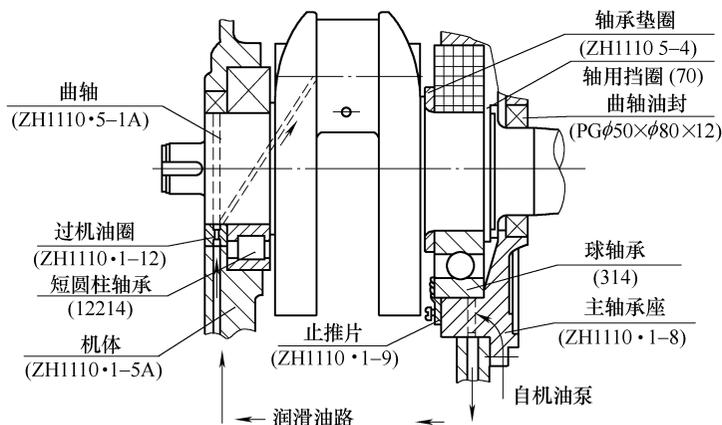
ZH1110 型、ZH1115 型柴油机曲轴飞轮组装配图
